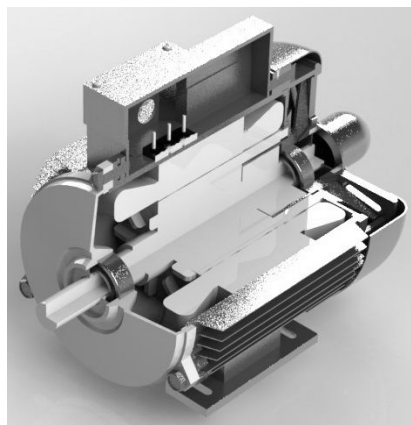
Внешний вид энергоэффективного двигателя улучшенной конструкции
